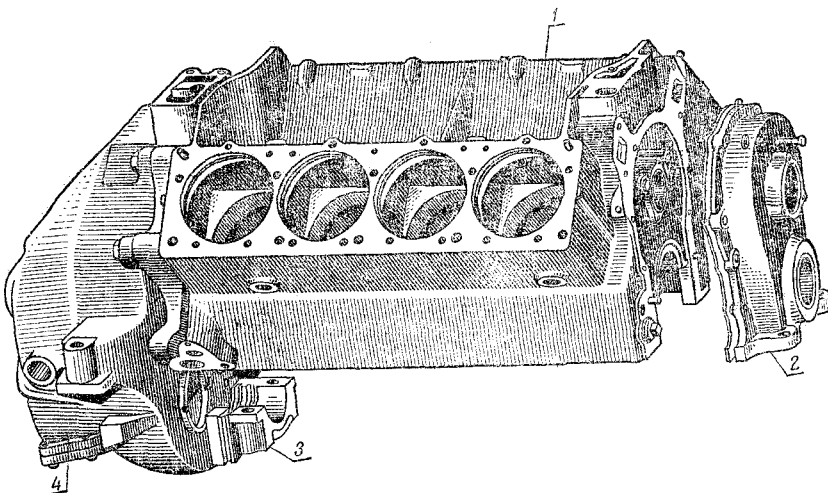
Блок-картер двигателя ЗИЛ-130:
